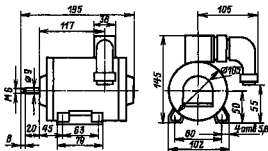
18 Габаритные и установочные размеры двигателя АА50-4
